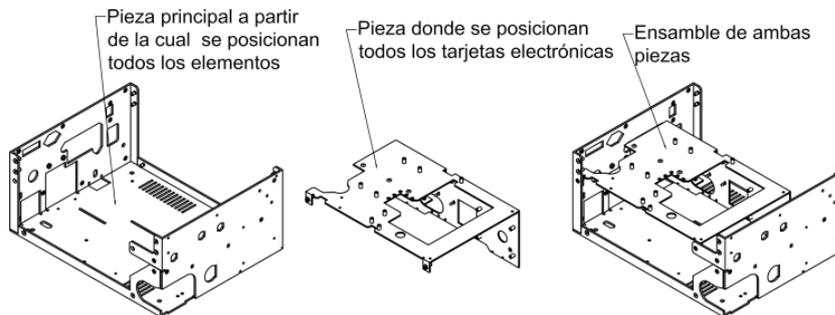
Diseño de la base principal y su ensamble con la base de tarjetas.
